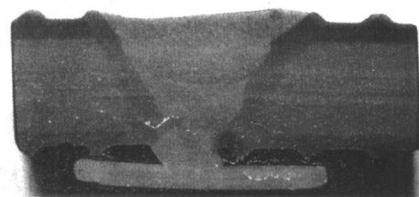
坡口焊接头纵截面宏观形貌
